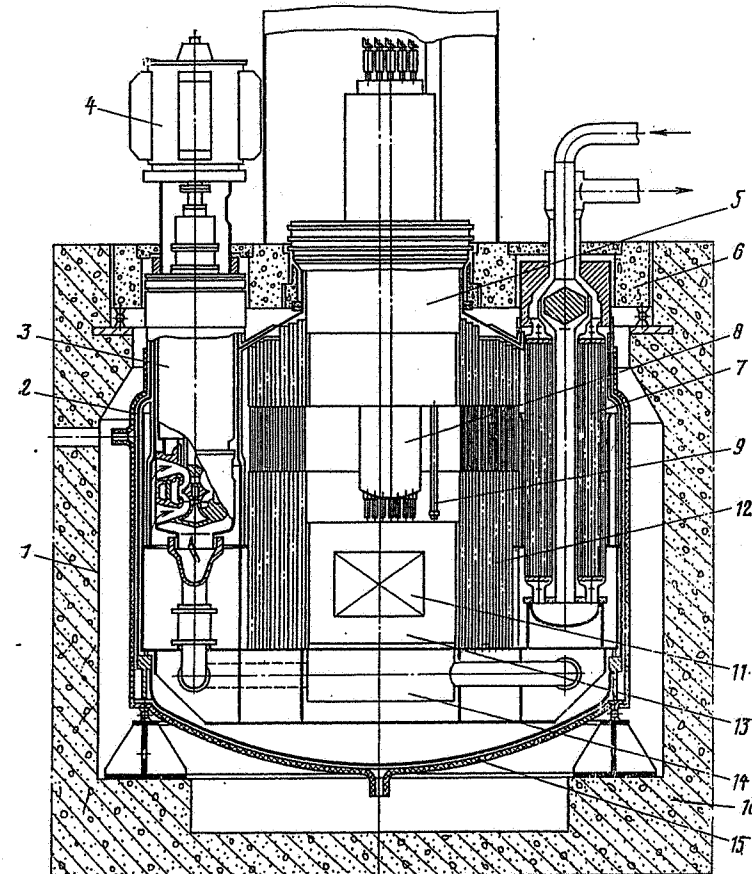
Схема реактора БН-600 (продольный разрез):
